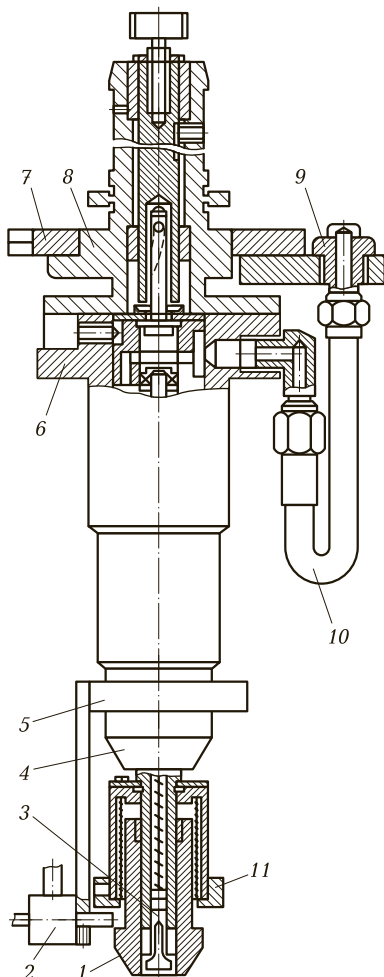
Инструмент для сборки резьбовых соединений:
